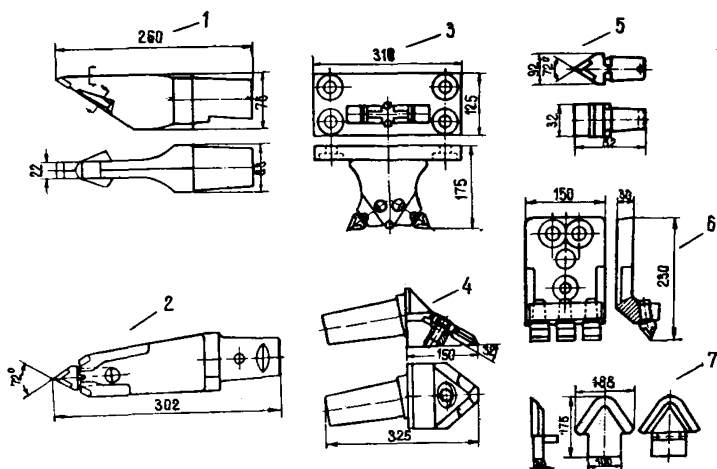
Резцы и ножи для струга УСБ-67:
